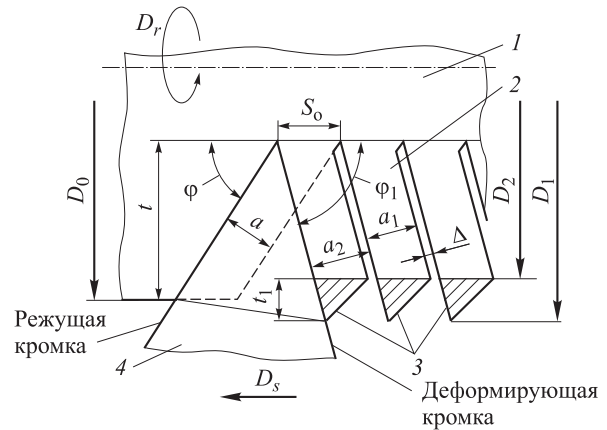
Схема формирования макрорельефа на наружной поверхности вала:
